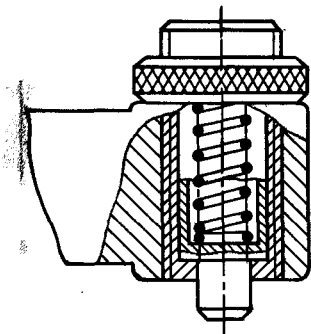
Ловитель для установки устройства относительно отверстия
